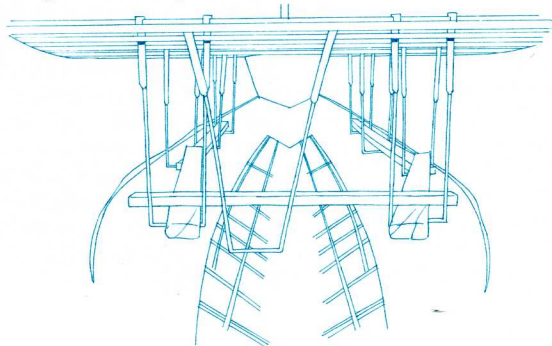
Le travail à l'intérieur d'un moule femelle exige l'installation de poutres suspendues à des trapèzes faits de fers en U (doc. Bouvier).
